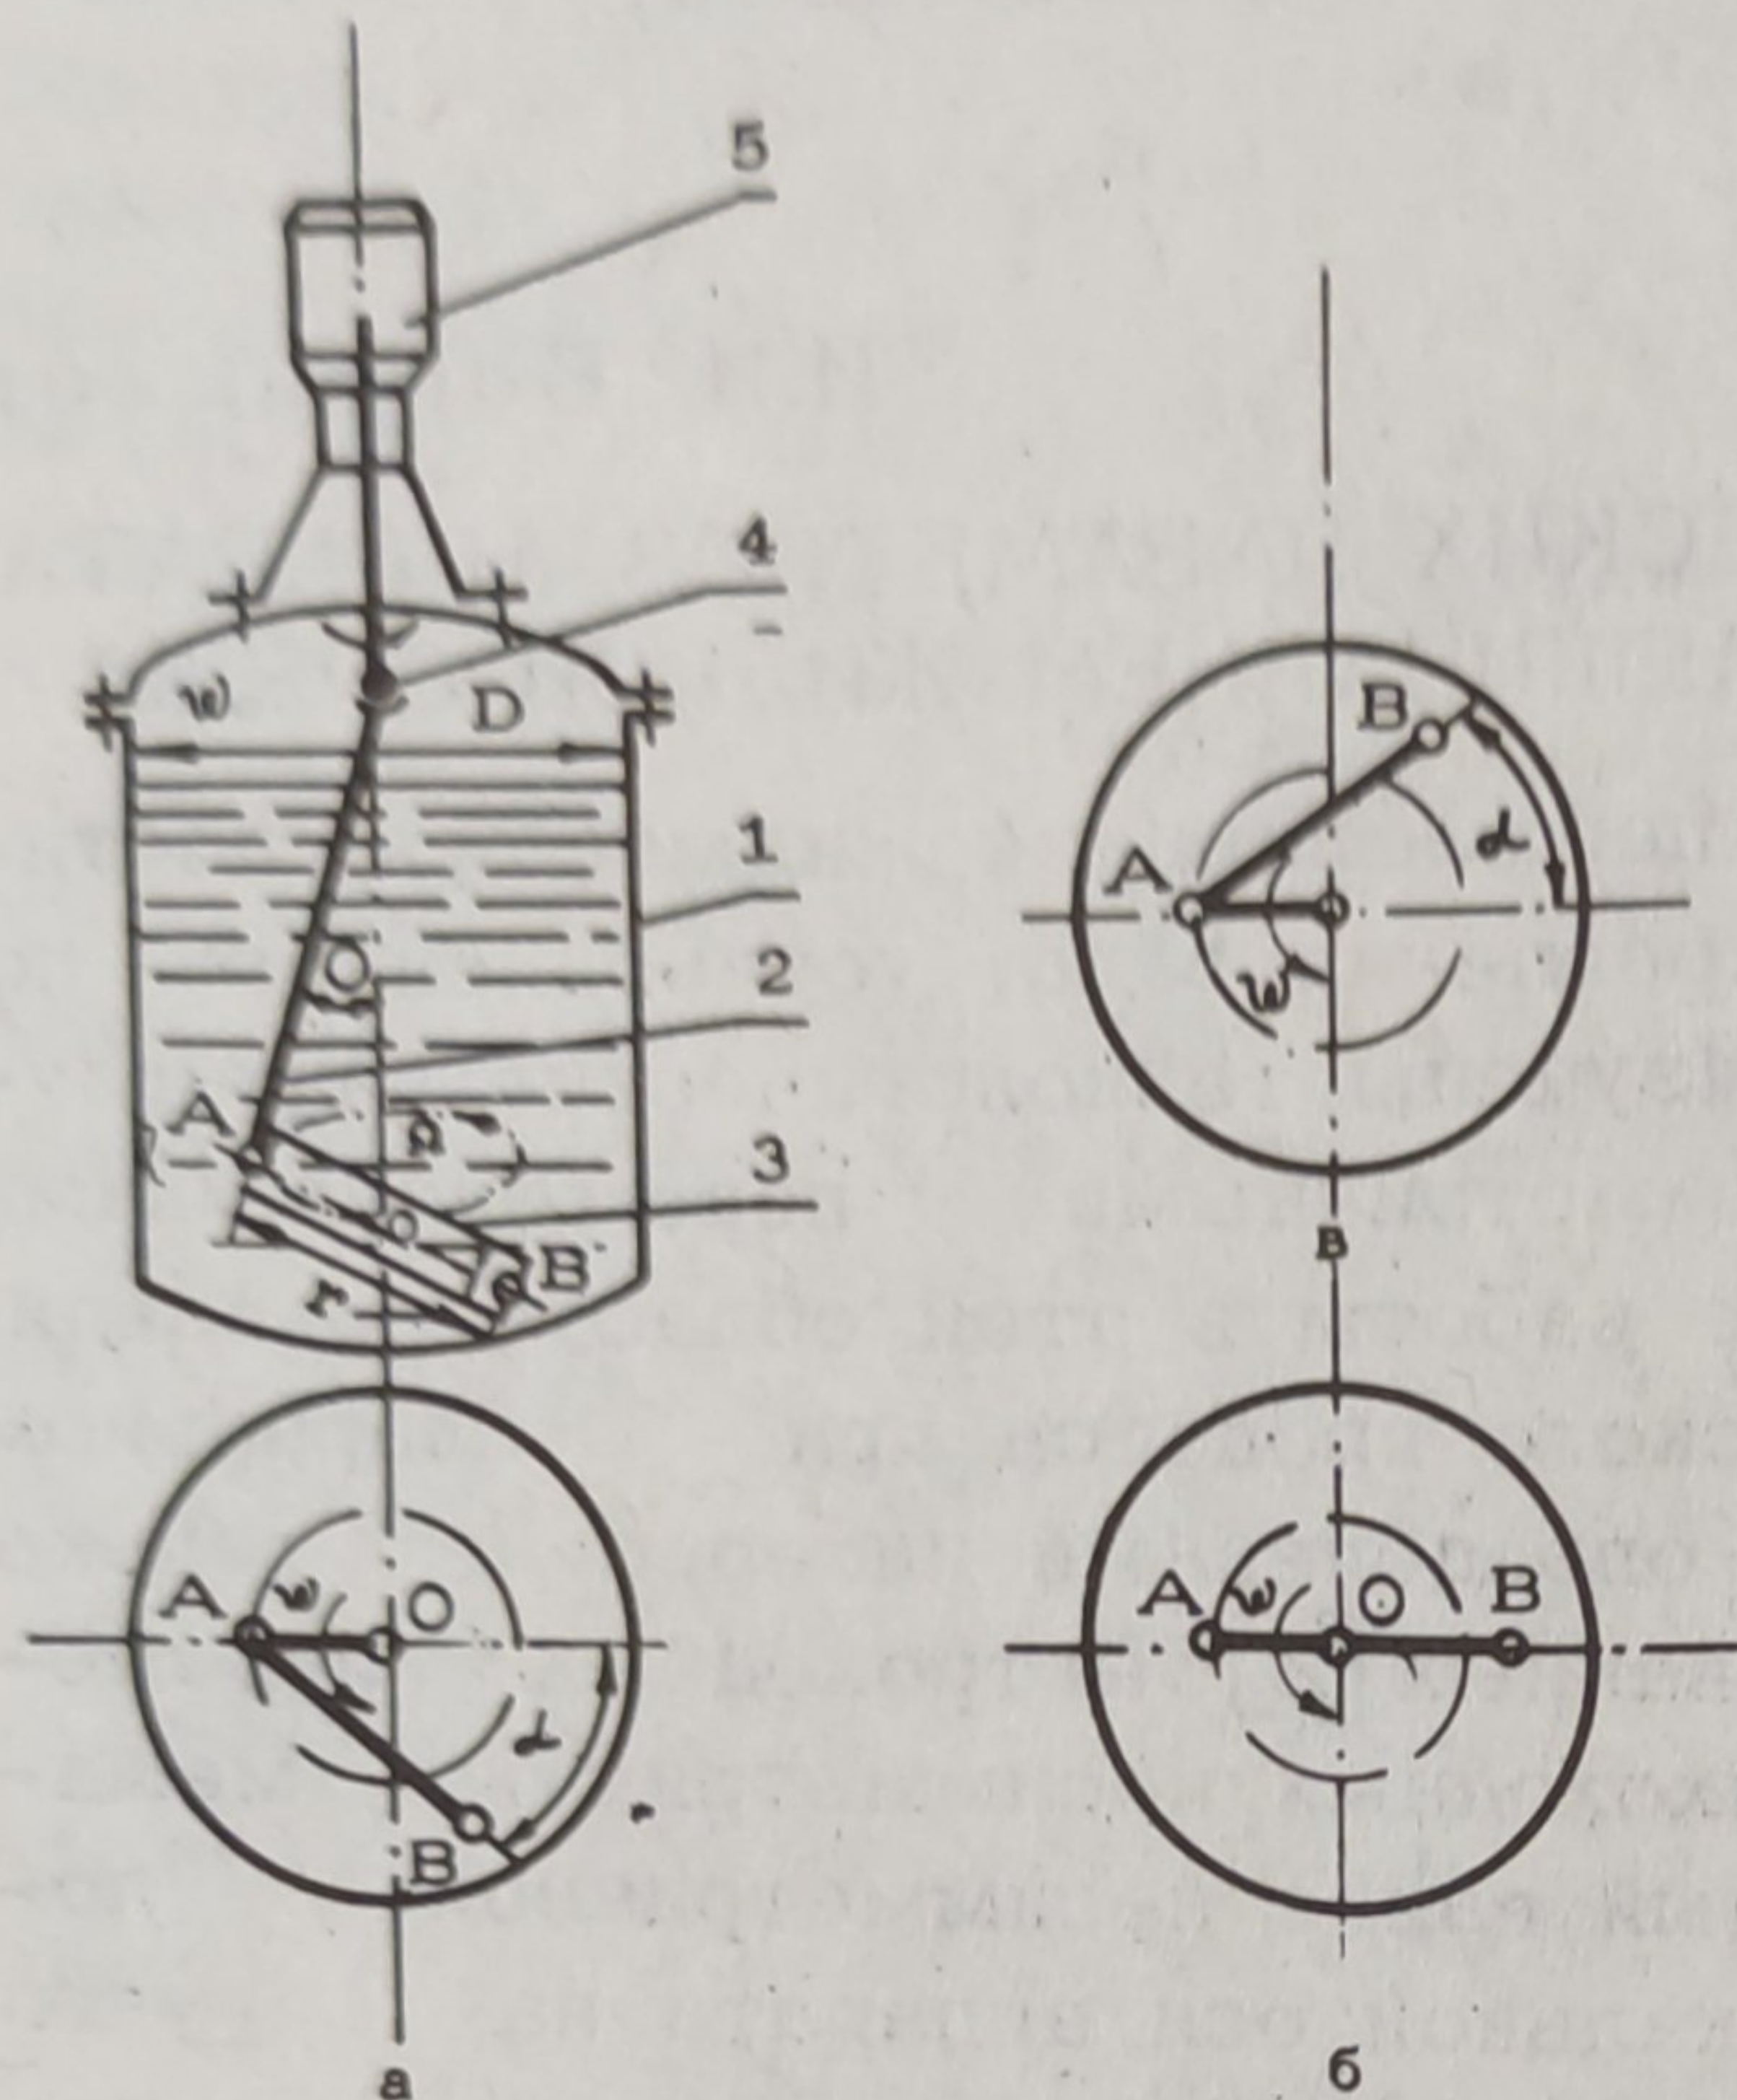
Схема аппарата с несимметрично шарнирно закрепленной мешалкой: а - докритический режим; б - критический режим; в - закритический режим; 1 - сосуд; 2 - вал; 3 - лопасть; 4 - универсальный шарнир; 5 - двигатель.
